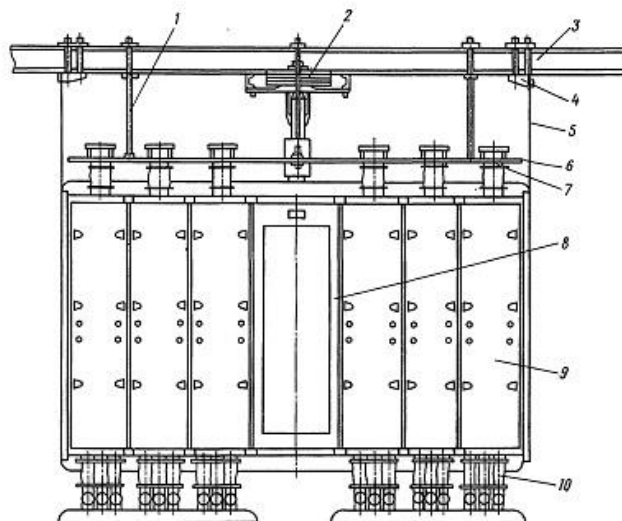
Рассев РЗ-БРБ: 1 — стержень, 2 — привод, 3 — рама; 4 — кронштейн; 5 — подвеска, 6 — плита, 7, 10 — приемные и выпускные устройства, 8 — корпус, 9 — дверь
